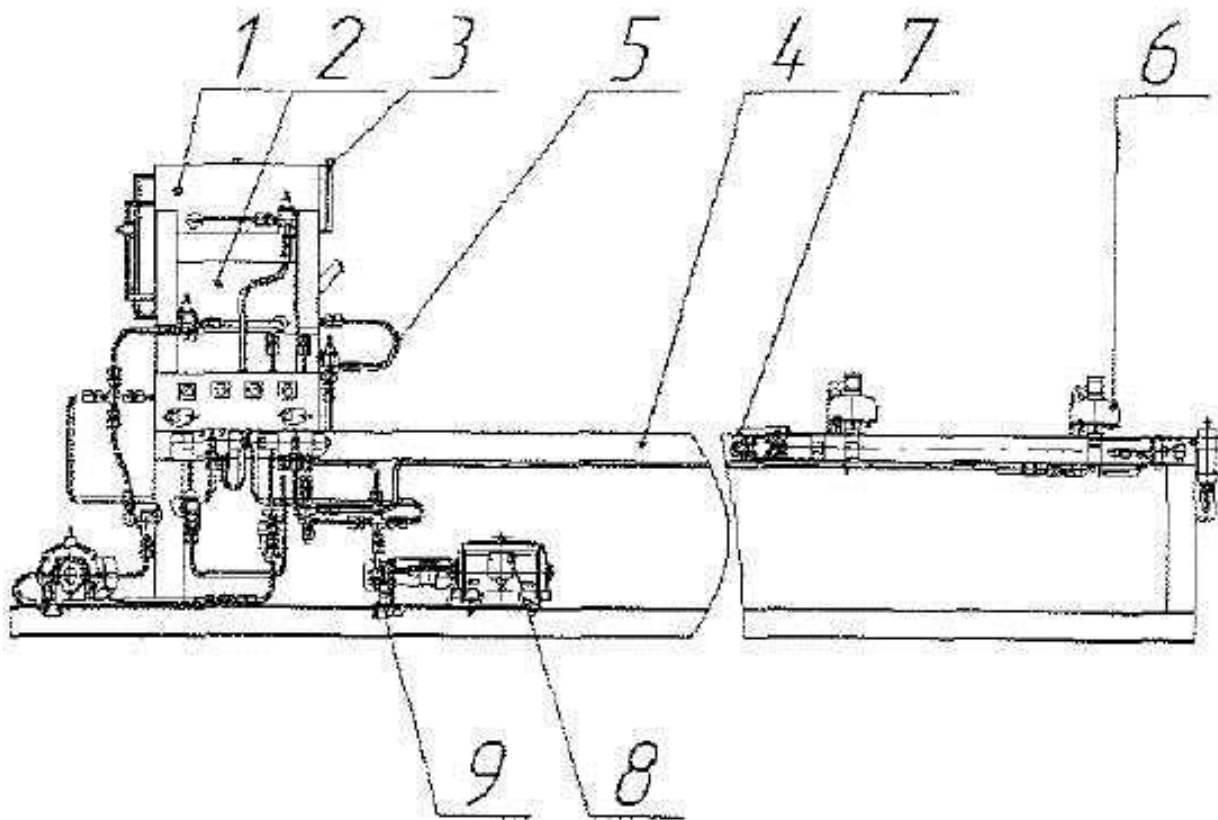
Стенд для испытаний подъёмных механизмов
